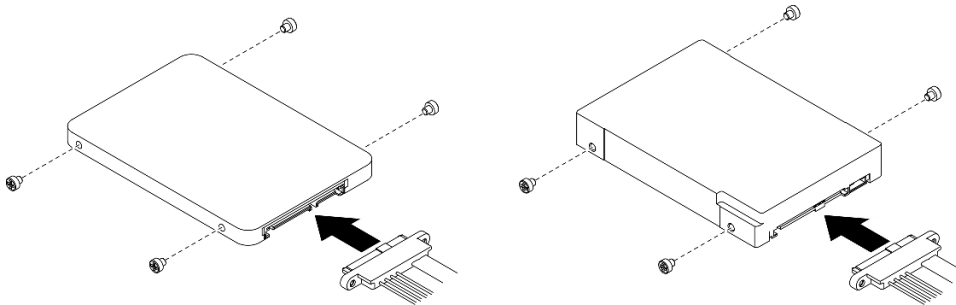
Installieren der Schrauben und Anschließen der Laufwerkkabel
